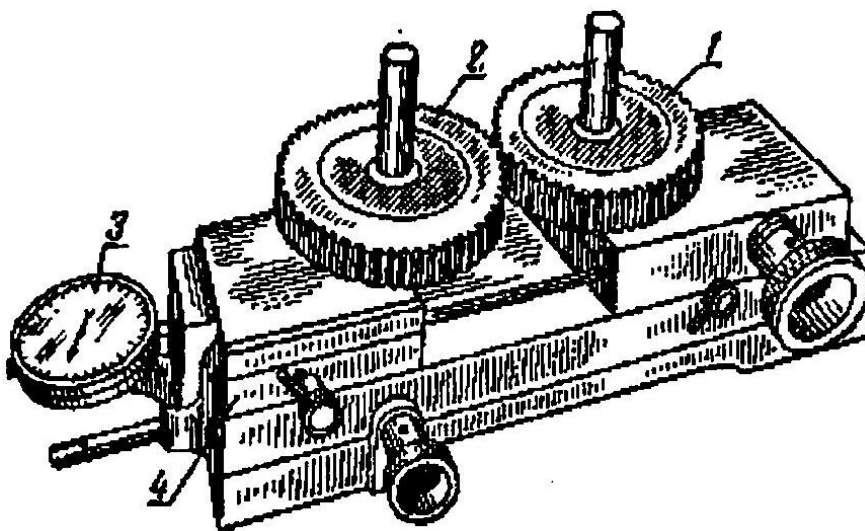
Приспособление для комплексного контроля зубчатых колес.
